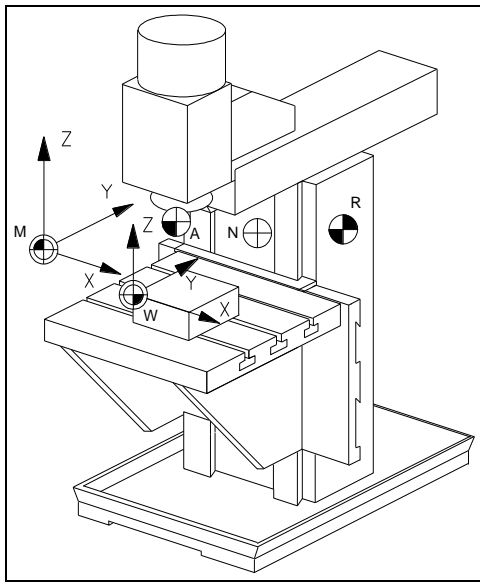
Установка нульової точки заготовки на вертикально фрезерному верстаті з ЧПК
